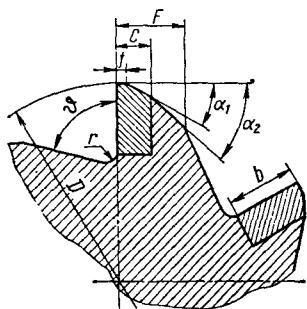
Профиль канавки развертки с твердосплавными напаянными пластинками
